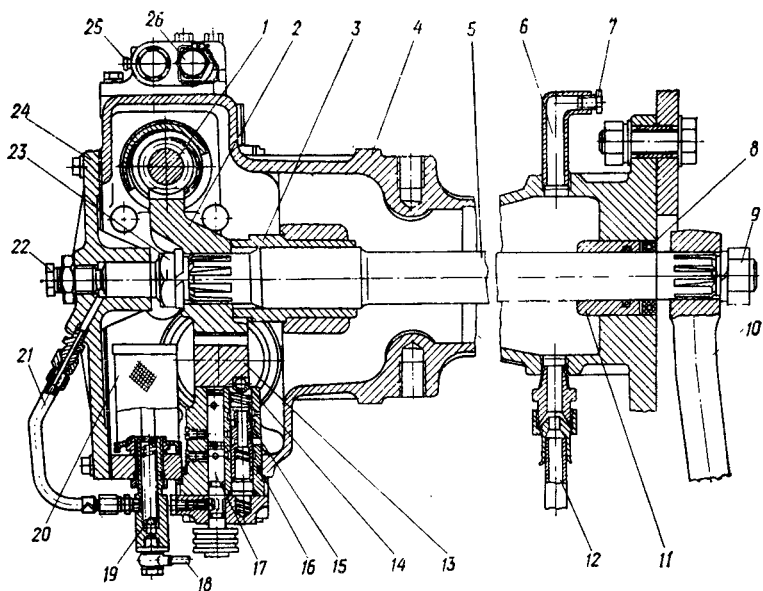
Гидроусилитель рулевого управления тракторов МТЗ-80/82:
